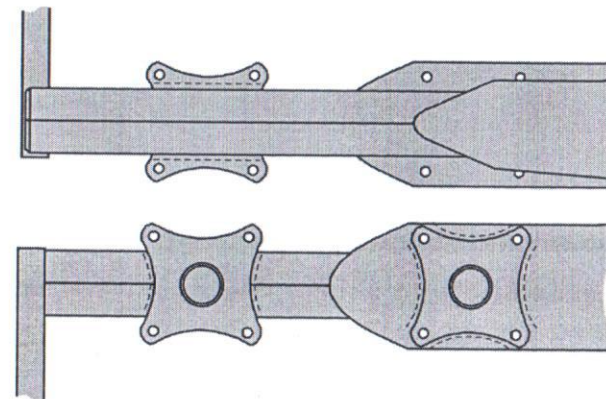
Контроль околошовной зоны сварного соединения опор шпинтона с продольной балкой рамы
